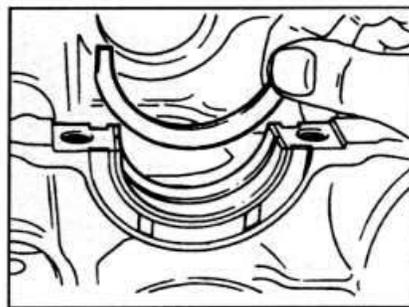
D.71. Установка полуовальных колец коленчатого вала смазочными канавками, направленными от блока цилиндров.
